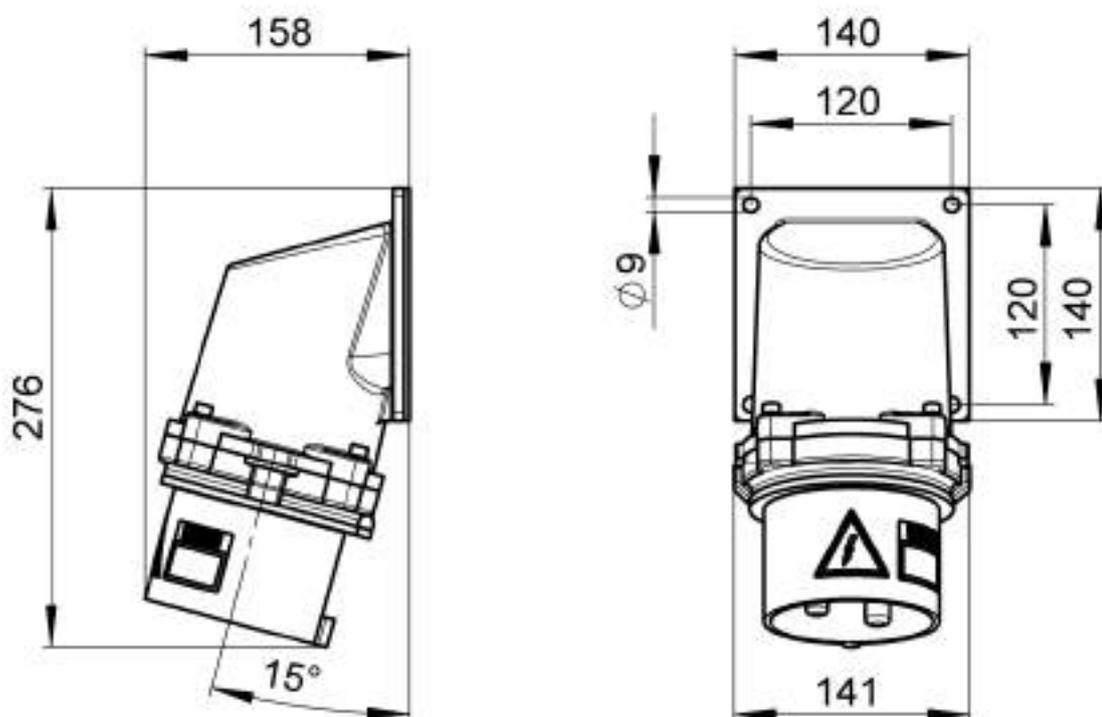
Abmessungen Anbaustecker (abgewinkelt) MCPA D-Line, C-Line (160A – 250 A) in mm
